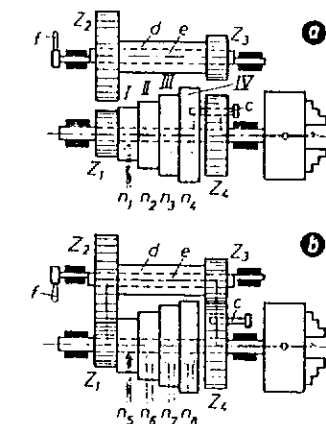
Mecanismo escalonado de cono de poleas con juego de engranajes: a) juego de engranajes desacoplado; b) juego de engranajes acoplado. El cono de poleas va firmemente unido a la rueda dentada Z_1 y gira con ésta loco alrededor del husillo del torno. La rueda Z_2 está enclavada firmemente al husillo del torno. Cuando el juego de engranajes está desacoplado, la fuerza de la correa es transmitida al husillo del torno por medio del perno de arrastre c . Para acoplar el juego de engranajes, el enlace del cono de poleas con Z_1 se deshace sacando el perno de arrastre. Las ruedas Z_3 y Z_4 están enlazadas mediante un casquillo d y giran sobre el árbol de acoplamiento e . Maniobrando una palanca f se hacen engranar con las ruedas Z_3 y Z_4 por medio de una espiga excéntrica. El flujo de fuerza pasa a través de Z_3 y Z_4 al husillo del torno.
